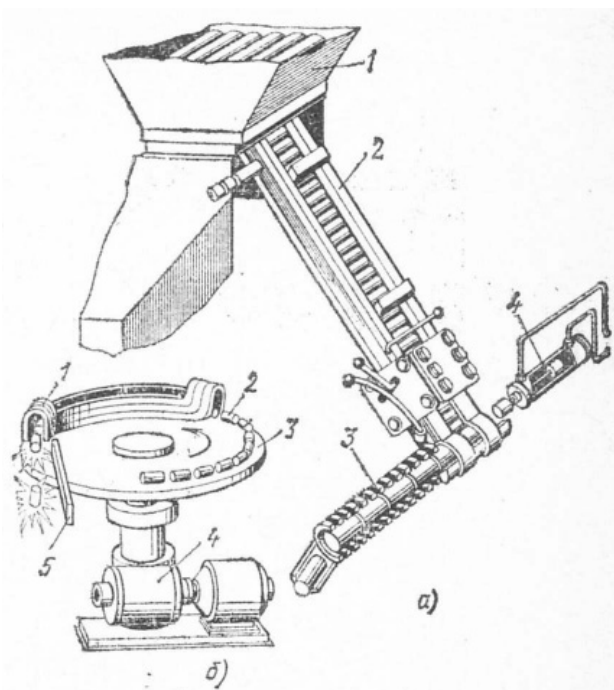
Методические индукционные установки для нагрева мерных цилиндрических заготовок: *а* – установка с толкателем; 1 – бункер для заготовок; 2 – наклонный лоток; 3 – индуктор; 4 – механизм загрузки; *б* – карусельная установка с шелевым индуктором; 1 – индуктор; 2 – заготовка; 3 – вращающий стол; 4 – механизм привода вращения стола; 5 – выбрасыватель заготовок
